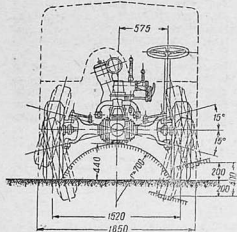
Кліренс увеличивается при установке дополнительного редуктора в ступице колес (автомобиль Зауэра)
